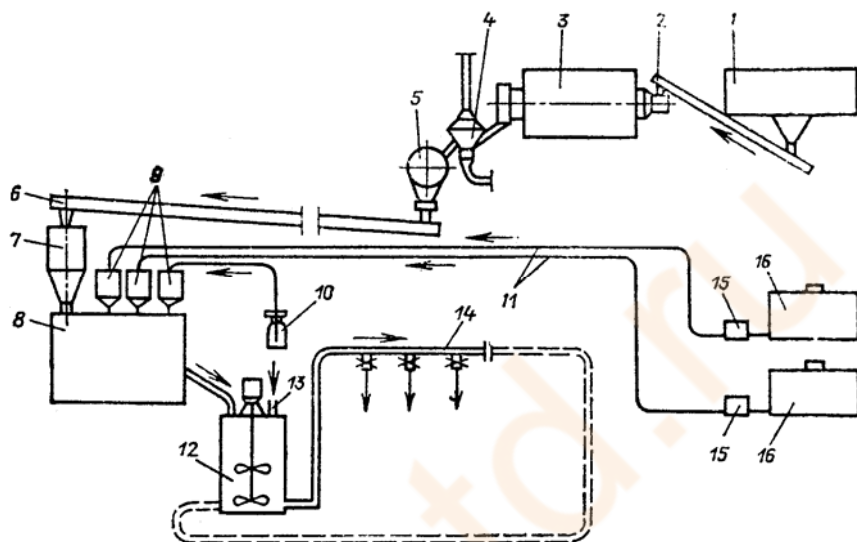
Схема комплексной механизированной линии приготовления суспензии: 1 – машина для вспарывания мешков; 2, 6 – закрытые конвейеры; 3 – печь; 4 – охладитель; 5 – сито; 7 – бункер; 8 – смеситель; 9 – напорные баки; 10 – емкость с кислотой; 11 – трубы; 12 – бак; 13 – патрубок; 14 – шланги; 15 – насосы; 16 – цистерны
